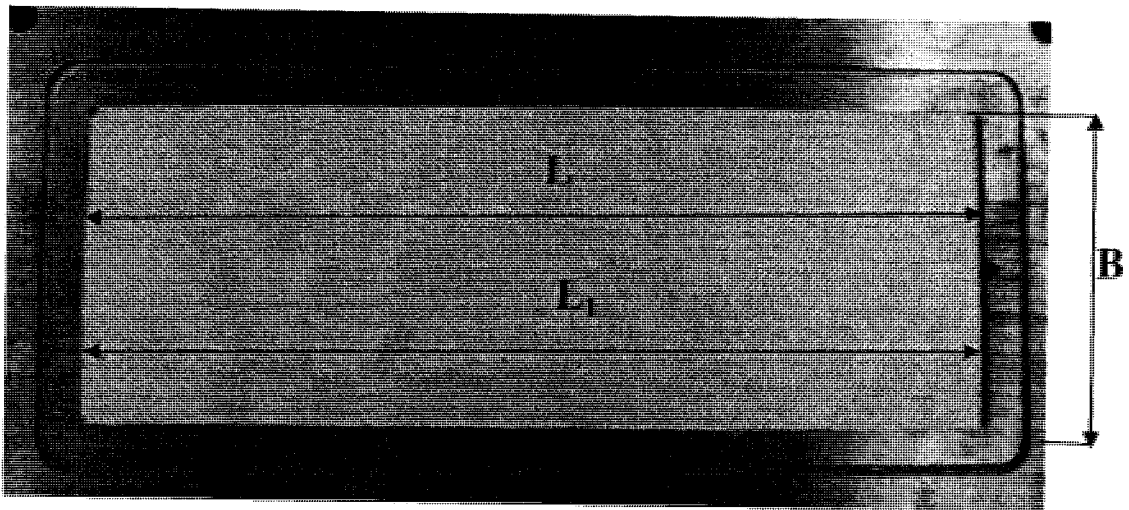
Dimensions de la préforme et de la cavité du moule.
